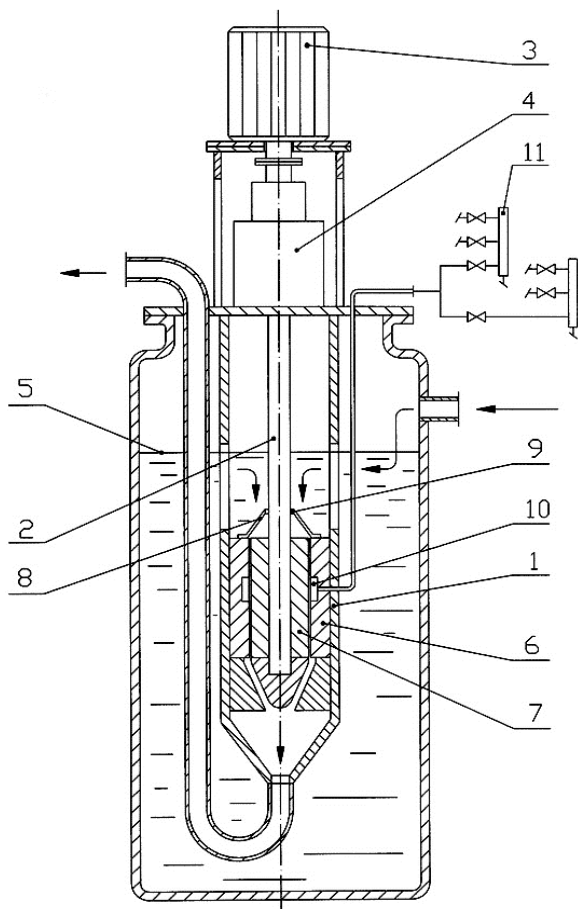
ЛГН для перекачування розплавленого металу: 1 – корпус; 2 – вал; 3 – привід; 4 – підшипниковий вузол; 5 – рівень середовища, що перекачується; 6 – втулка; 7 – гвинт; 8 – конічна сітка; 9 – радіальний зазор; 10 – кільцева камера; 11 – колектори
